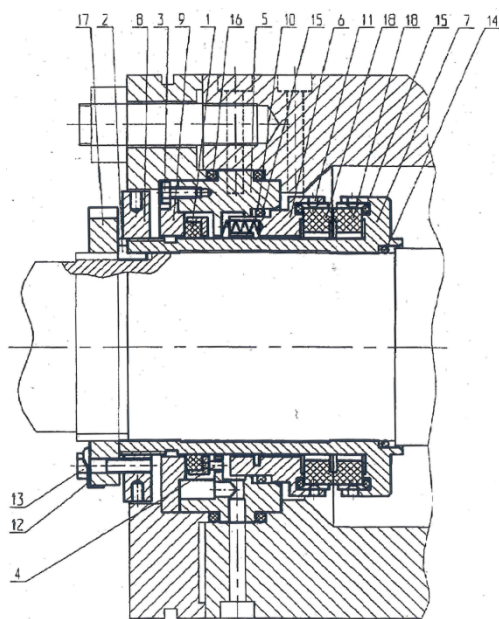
Торцевое уплотнение: 1 – уплотнение резервное; 2 – шпонка; 3 – болт; 4 – штифт; 5 – корпус; 6 – обойма; 7 – гильза; 8 – гайка круглая; 9 – крышка; 10 – пружина; 11 – поводок; 12 – шайба стопорная, 13 – болт; 14, 15, 16 – кольца уплотнительные; 17 – гайка круглая; 18 – кольцо
